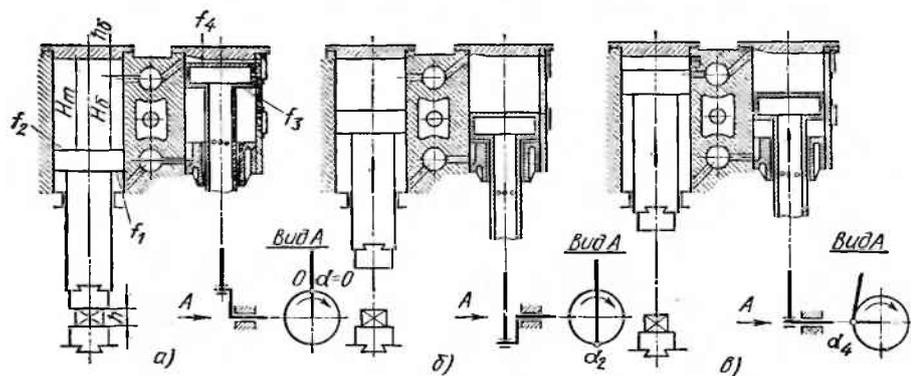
Различные положения (а—в) поршней рабочего и компрессорного цилиндров
